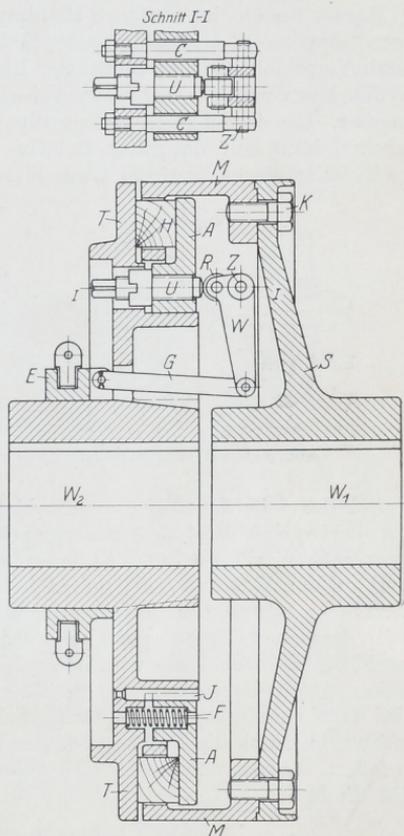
Reibkupplung der Transmissionswerke Fr. Flender & Co., Düsseldorf.
